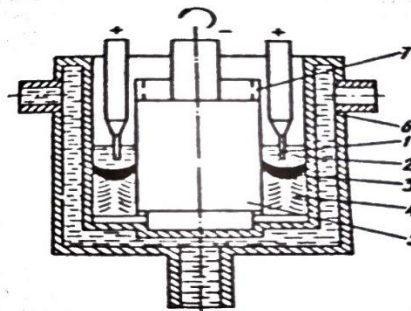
ЕШН циліндричної зовнішньої поверхні при малій довжині утворюючої:
